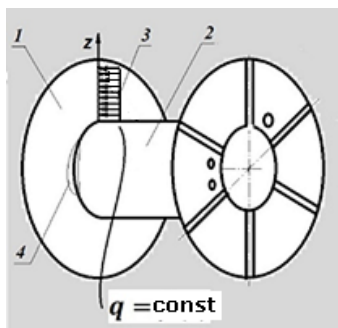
Схема конструкции пластиковой катушки и нагрузки на боковину
